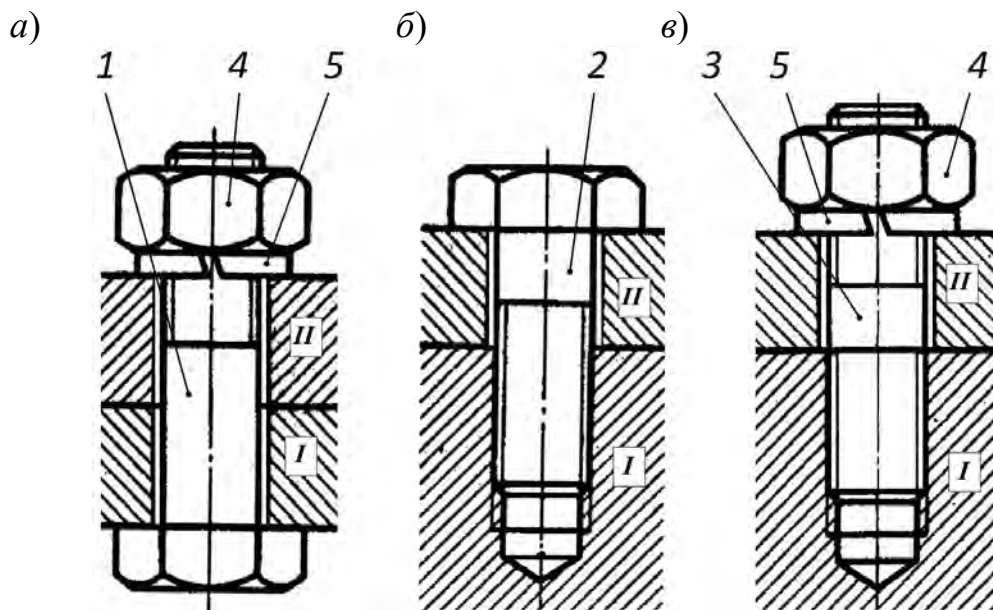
Виды резьбовых соединений: *а* – болтовое; *б* – винтовое; *в* – шпильчное; *1* – болт; *2* – винт; *3* – шпилька; *4* – гайка; *5* – шайба; *I* и *II* – соединяемые детали
